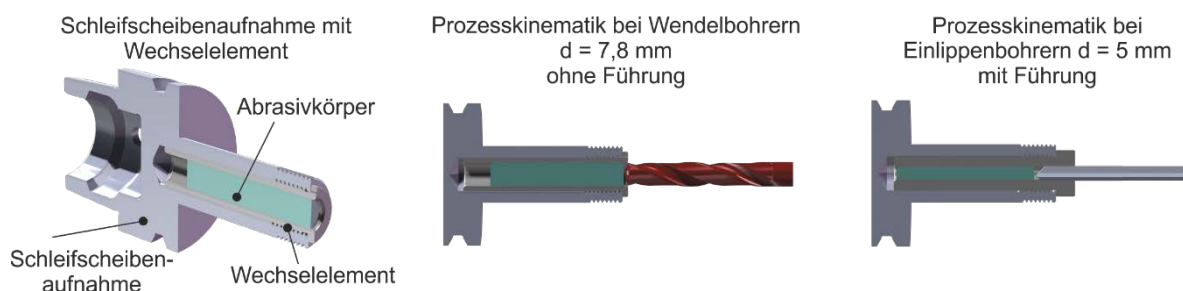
Varianten der Schneidkantenpräparation Schaftwerkzeuge mit einem elastisch gebundenen Abrasivkörper auf einer Werkzeugschleifmaschine
